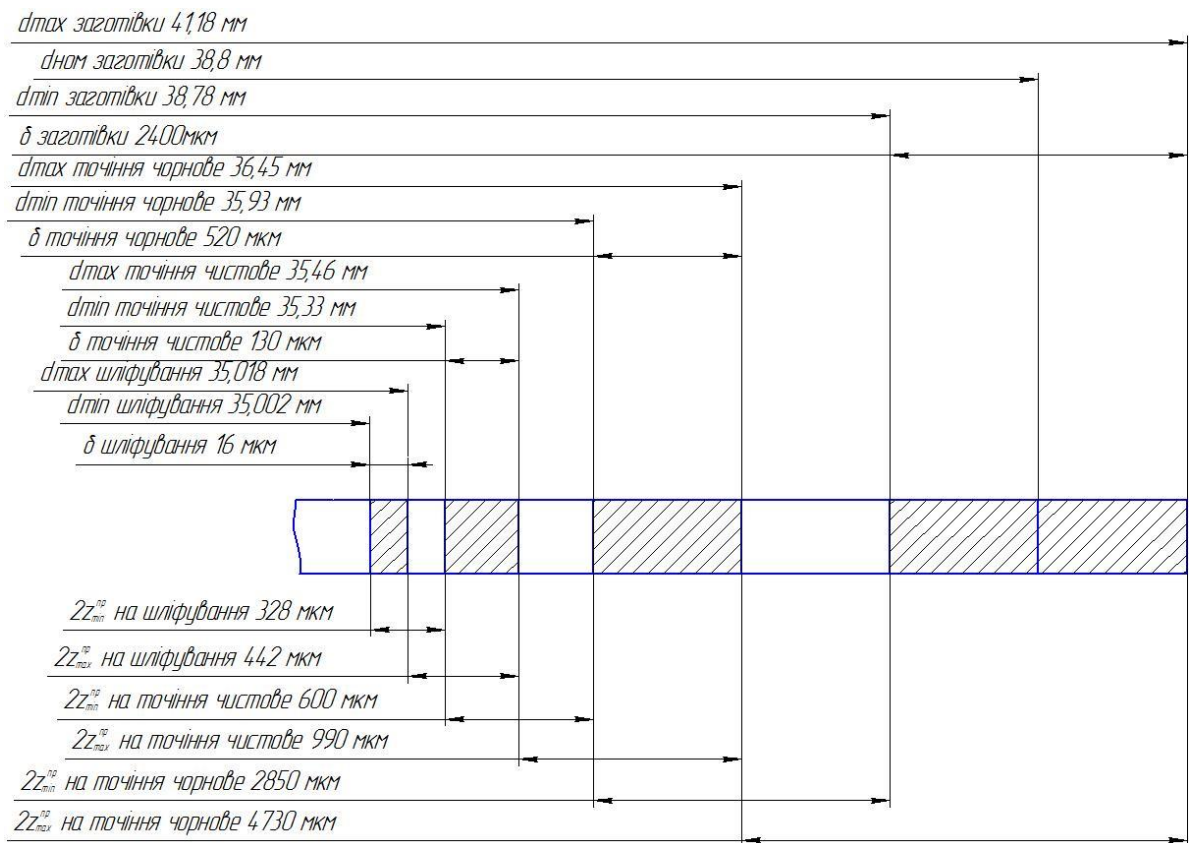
Схема графічного розташування припусків і допусків на обробку зовнішньої поверхні $\varnothing 35k6$
